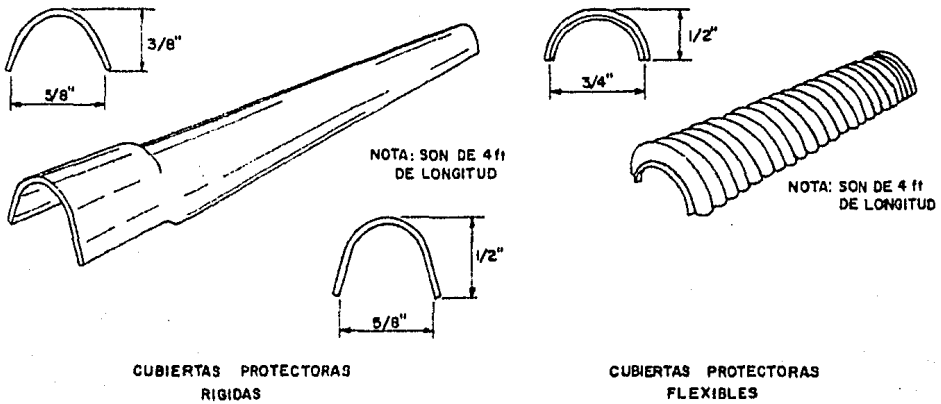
CUBIERTAS PROTECTORAS PARA CABLES DE CALENTAMIENTO ( RIGIDAS Y FLEXIBLES).
